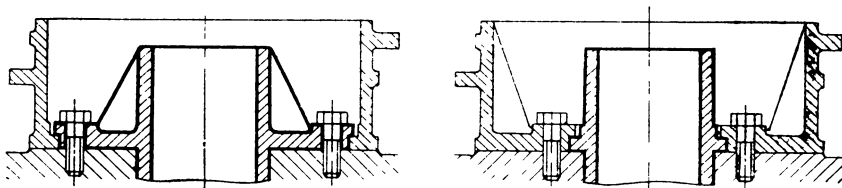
Уменьшение центрирующего диаметра в соединениях корпусных деталей
